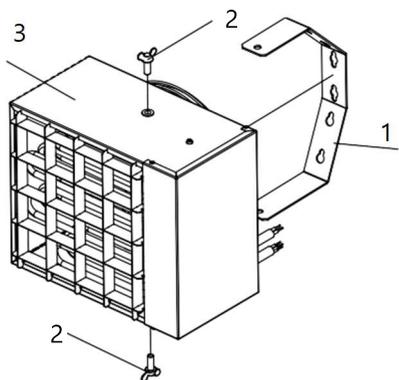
Installation du support mural pour OLO-F5, OLO-F9
